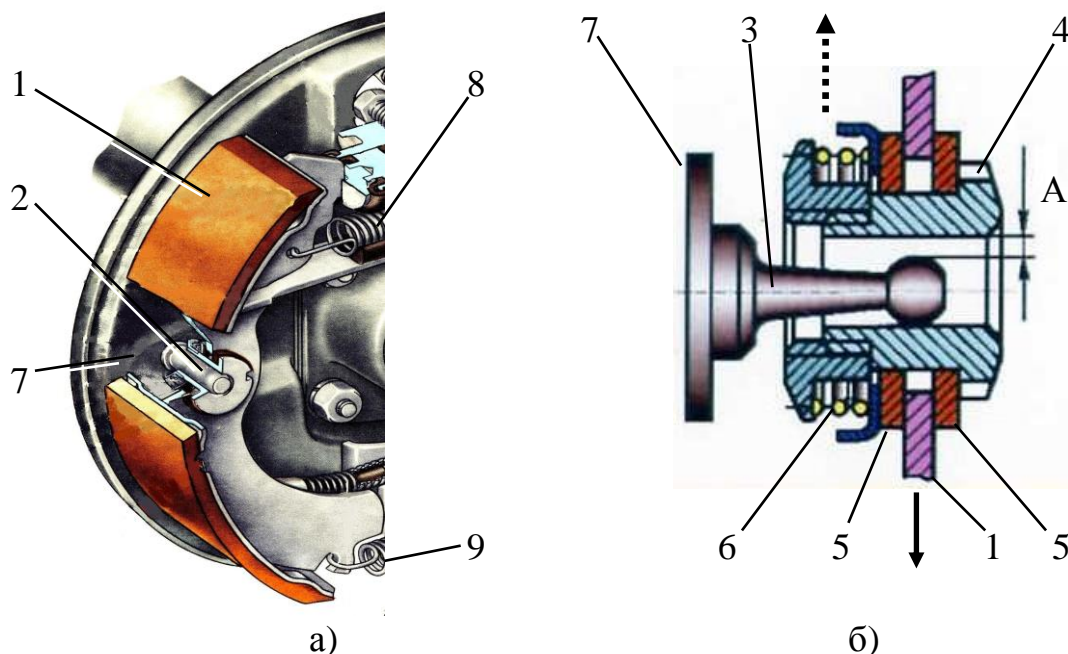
Барабанный тормозной механизм с регулировкой зазора между тормозной колодкой и барабаном фрикционными шайбами (а), конструкция регулировочного устройства (б): 1 – тормозная колодка; 2 – регулировочное устройство; 3 – стойка; 4 – корпус регулировочного устройства; 5 – фрикционные шайбы; 6 – пружина; 7 – опорный диск тормозного механизма; 8 и 9 – стяжные пружины тормозных колодок; А – зазор
